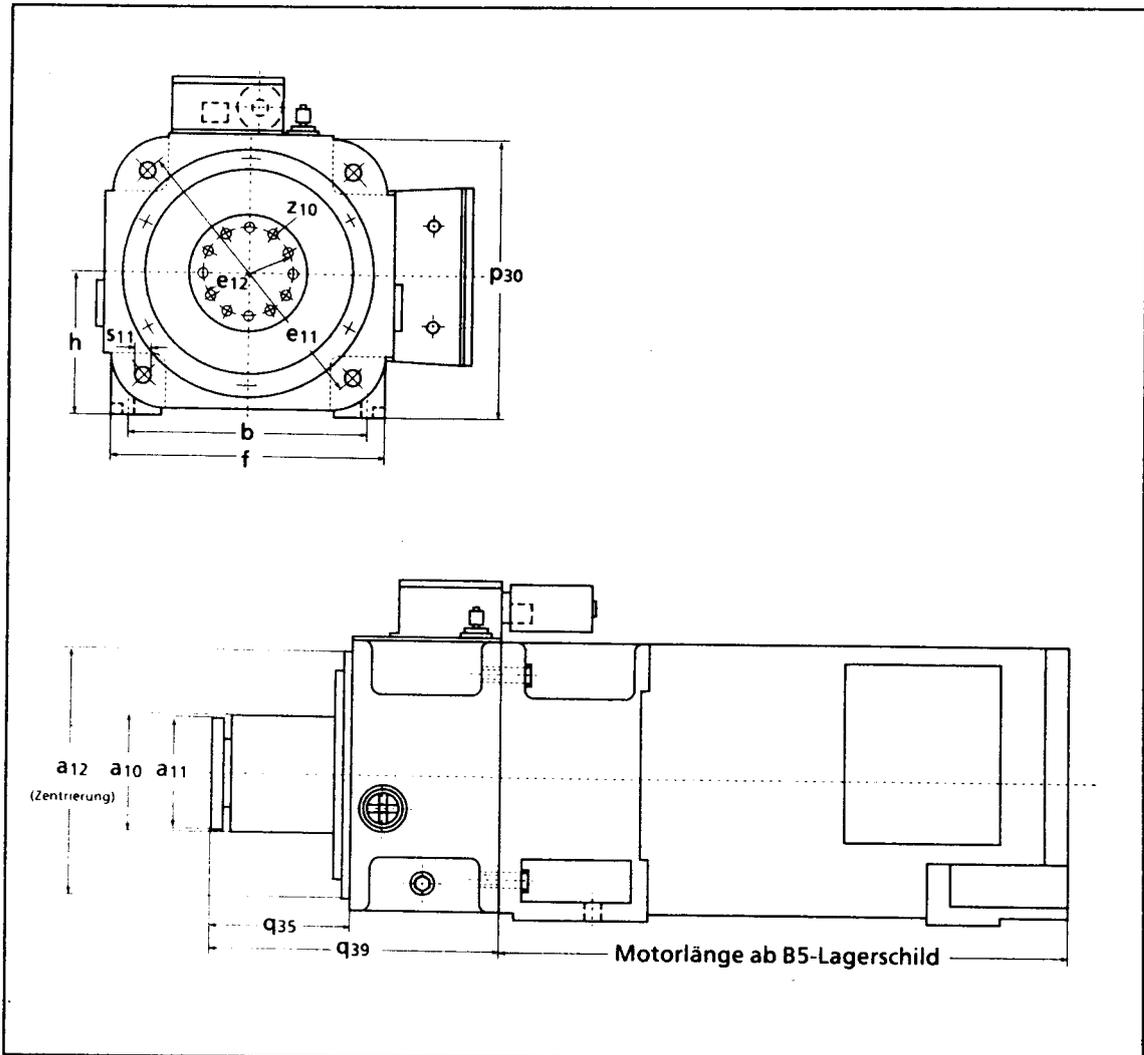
Drehstrommotor mit Schaltgetriebe
